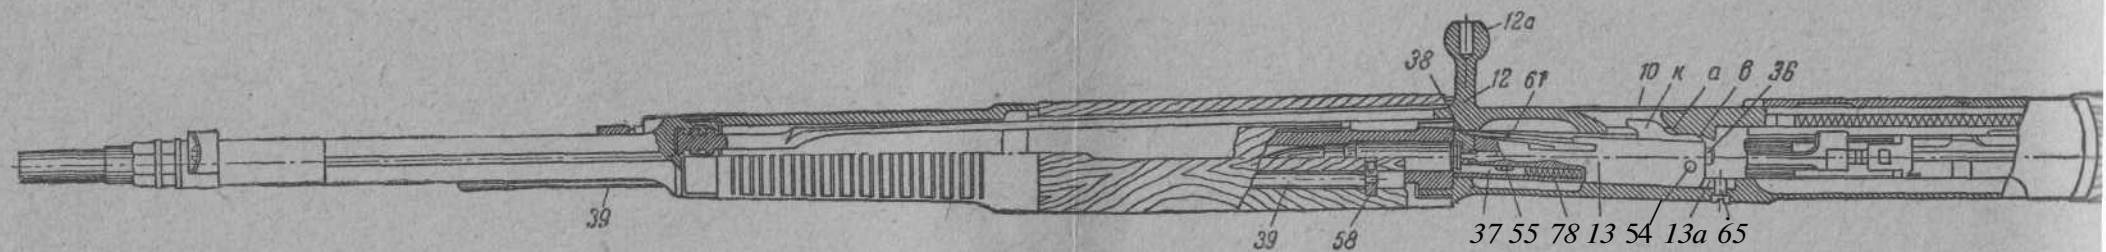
Вид винтовки ЗН-29 (затвор заперт).
